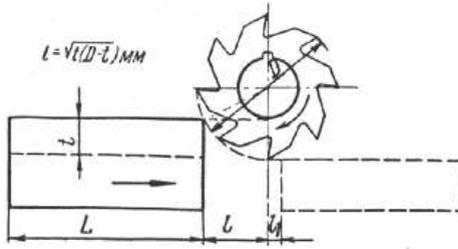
Врезание и перебег цилиндрической фрезы
